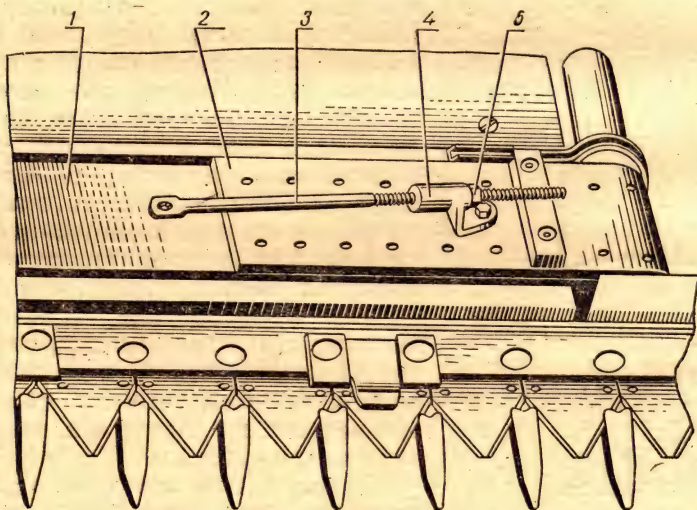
Приспособление для соединения прорезиненных лент ременно-планчатого транспортера:
